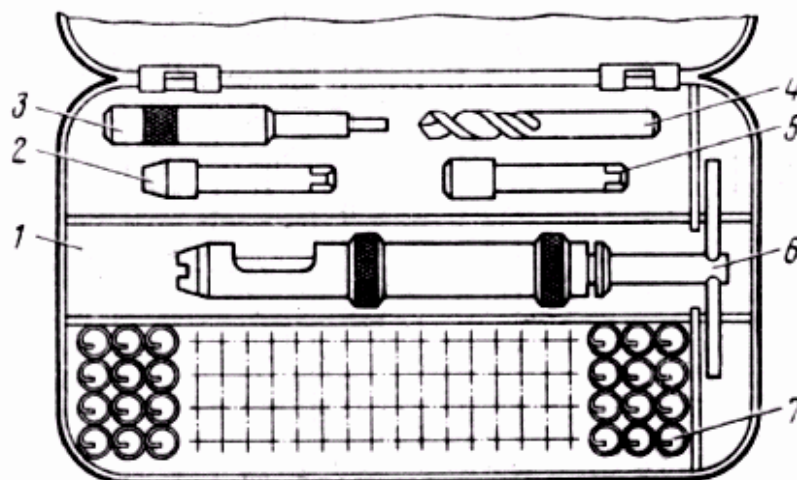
Комплект приспособлений для ремонта резьбовых отверстий спиральными вставками:
